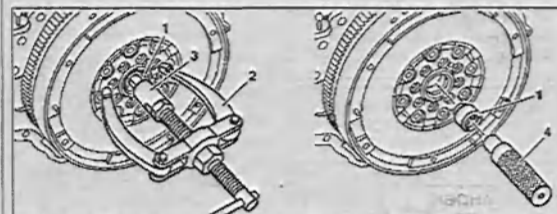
Снятие и установка направляющего подшипника в маховике:
